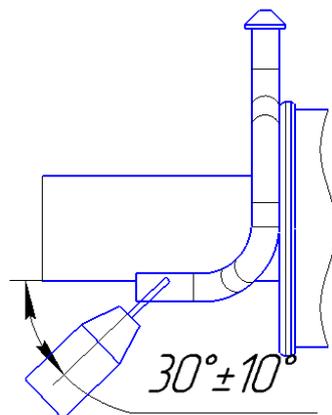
Сварка глушителя дополнительного и кронштейна
